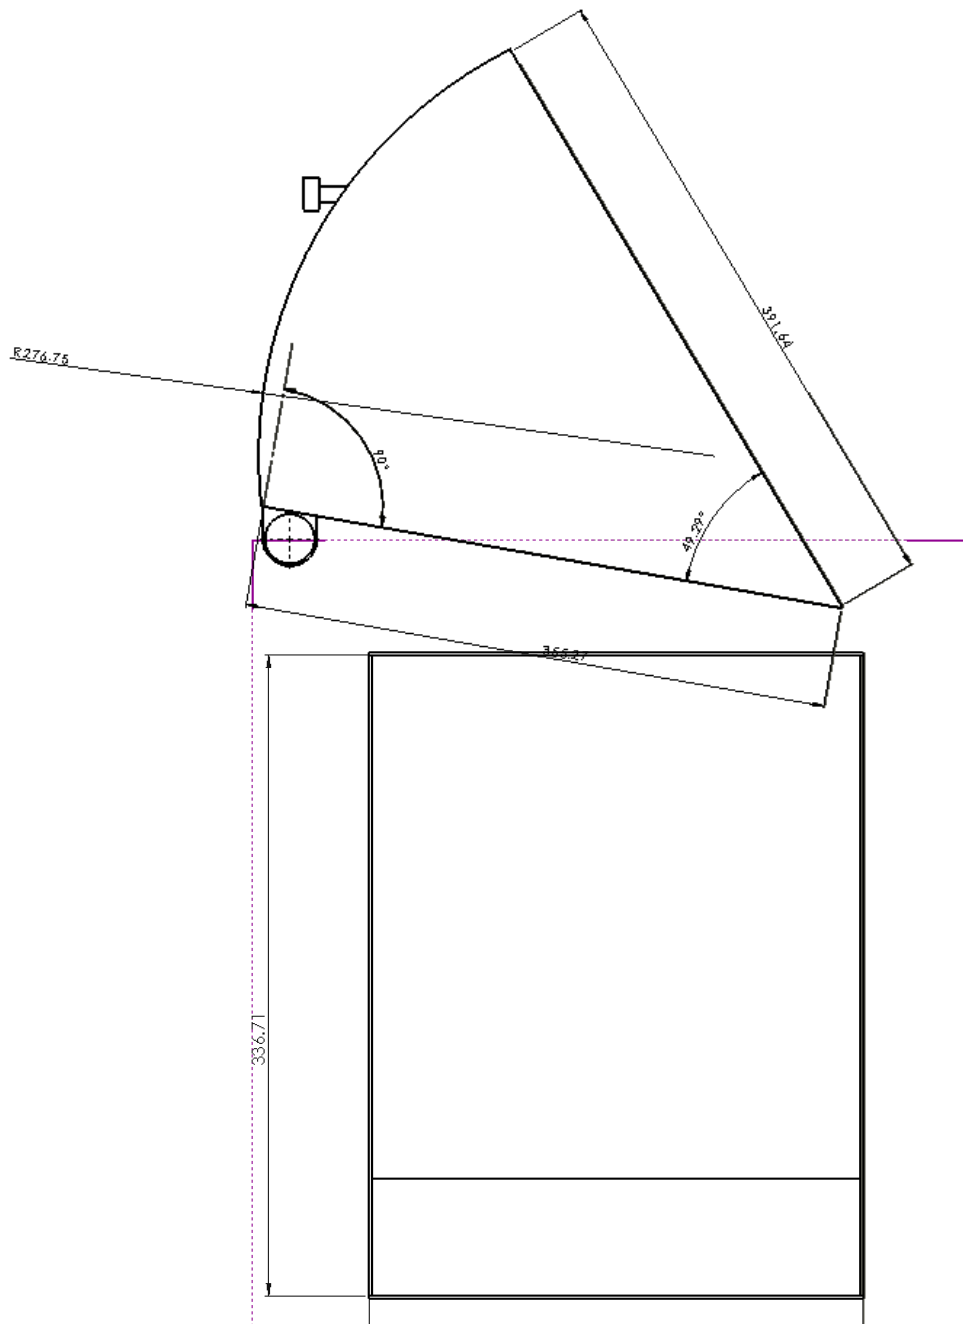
Plano Compuerta. Fuente: Elaboración propia
